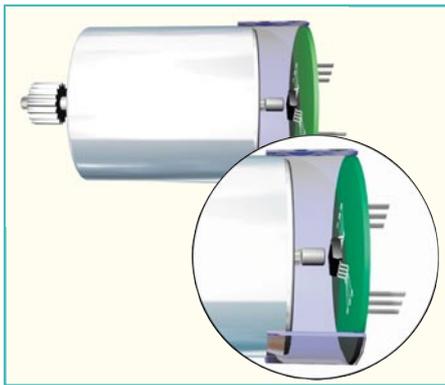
Positionsabfrage eines Elektromotor-Rotors
